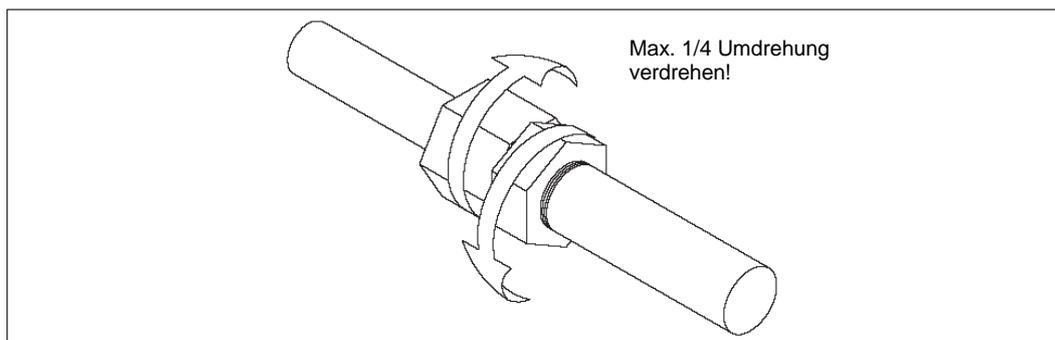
Klemmverschraubung der Quick Set Pumpe
